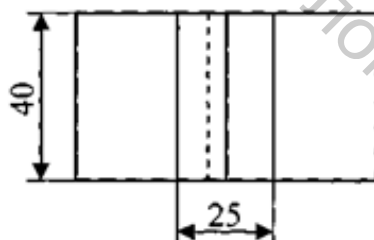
Образец для испытания прочности ниточных швов
